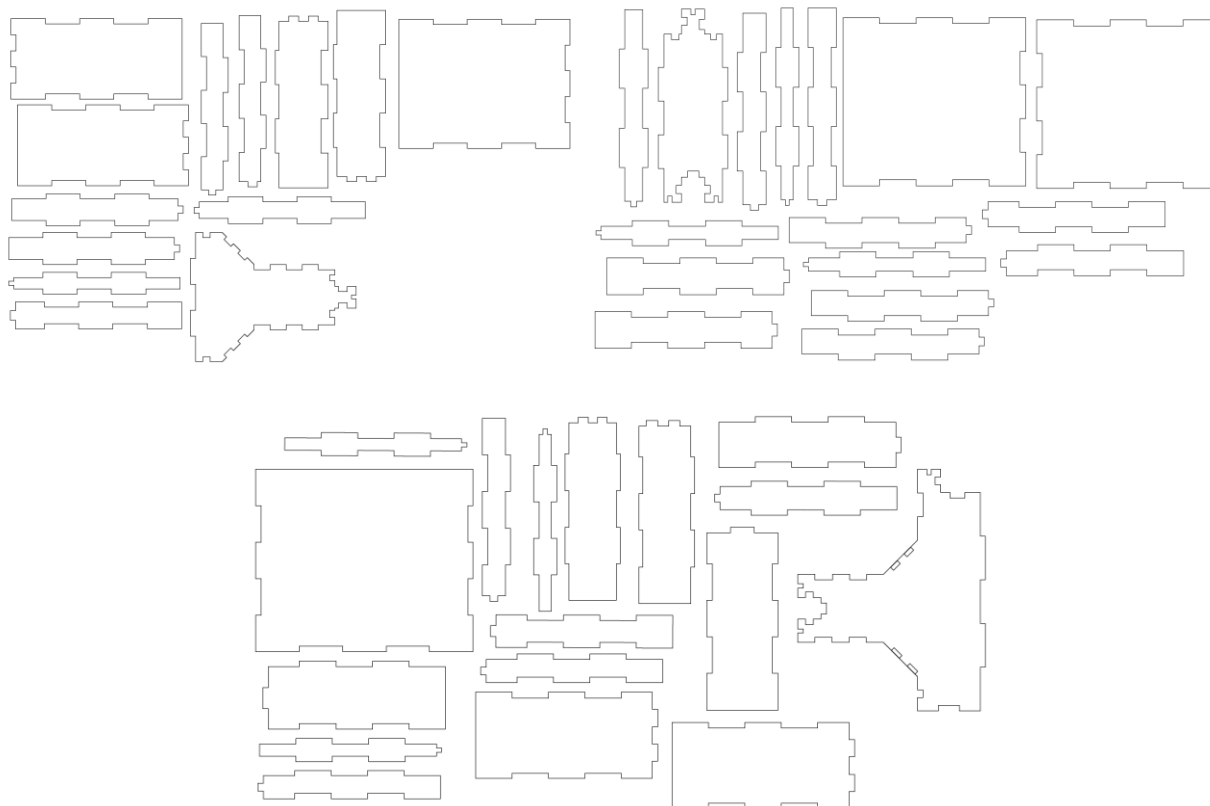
la modélisation de la découpe des surfaces planes des moules
